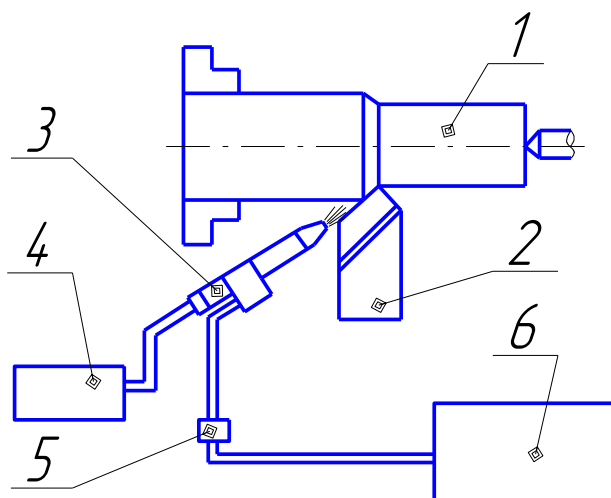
Схема подачі ІГС в зону різання: 1 – заготовка, 2 – інструмент, 3 – плазматрон-сопло, 4 – система живлення плазматрону, 5 – регулятор тиску газового середовища, 6 – компресор.
